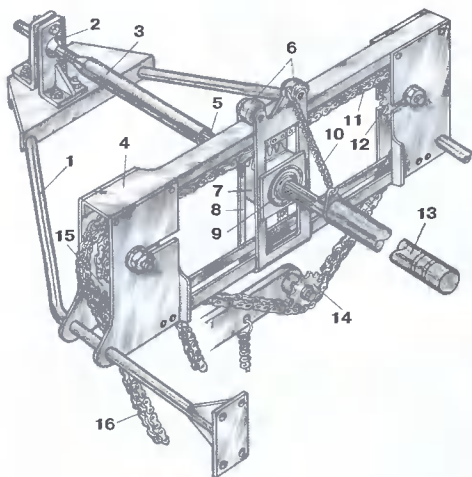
Механизм привода: 1 — рама, 2 — шарнир для рычага, 3 — тренинг-рычаг, 4 — корпус механизма, 5 — шлицевой вал, 6 — ролики, 7 — зацеп, 8 — синхронизатор, 9 — главный шарнир, 10 — пружина, имитирующая вес весла, 11 — обводная цепь, 12 — звездочка обводной цепи, 13 — рукоятка тренинг-рычага, 14 — натяжная звездочка, 15 — ведущая звездочка и муфта проскальзывания, 16 — рабочая цепь.
